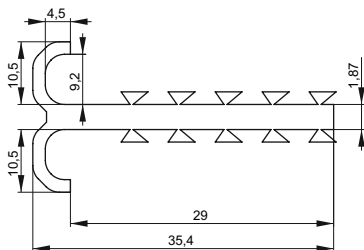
Габаритные размеры хомута Т-обр. / Figure 3 – Overall dimensions of the clamp T-shaped 4–12 mm
